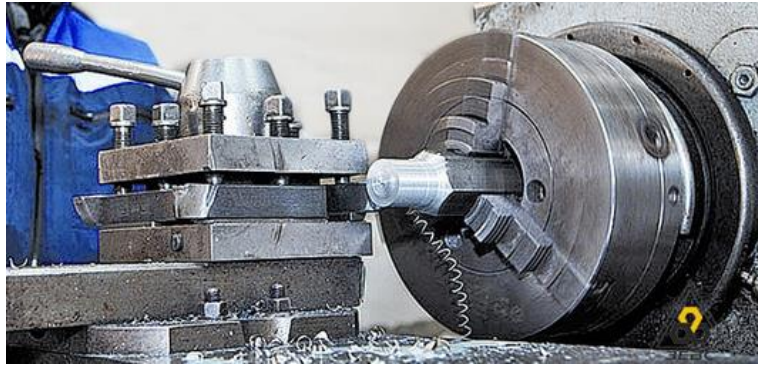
Виготовлення болта на токарно - гвинторізальному верстаті
